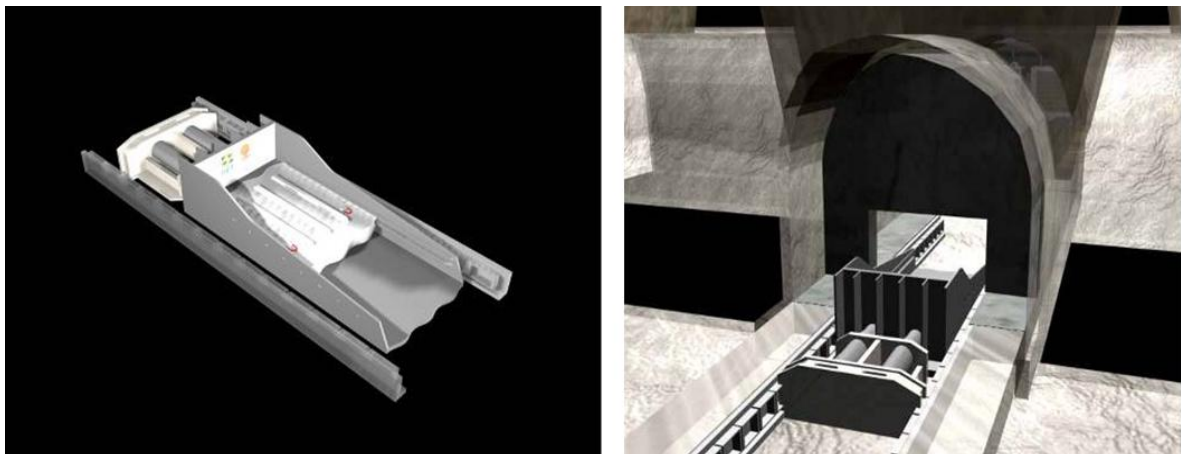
Esquema de Dozer: (Izquierda) Vista isométrica de Dozer y placas que lo componen; (Derecha) Vista posterior del Dozer ubicado en un punto de extracción (JRI, 2010)
